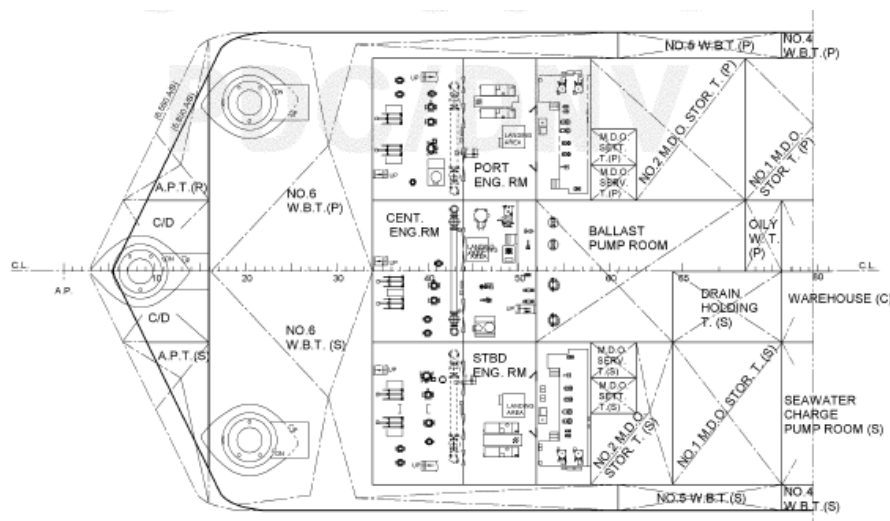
Planos del Buque de Perforación – 2ª Cubierta, 3ª Cubierta y Planta (Popa)
